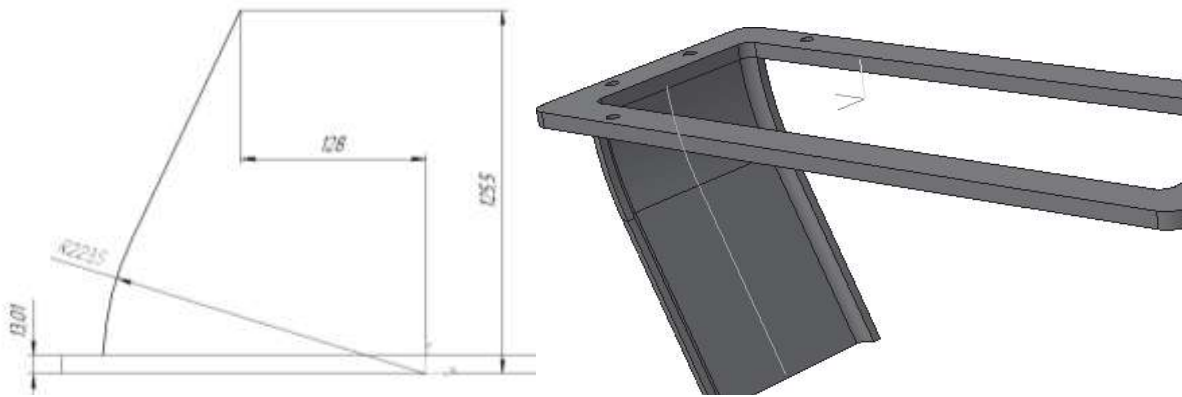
Додання передньої стінки корпусу редуктора
